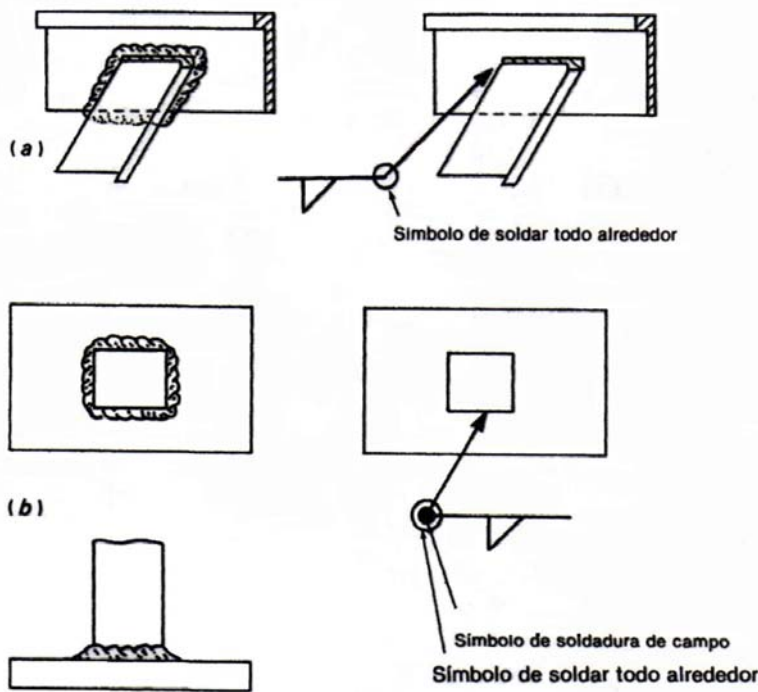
Símbolo de soldar todo alrededor y símbolo de soldadura de campo
